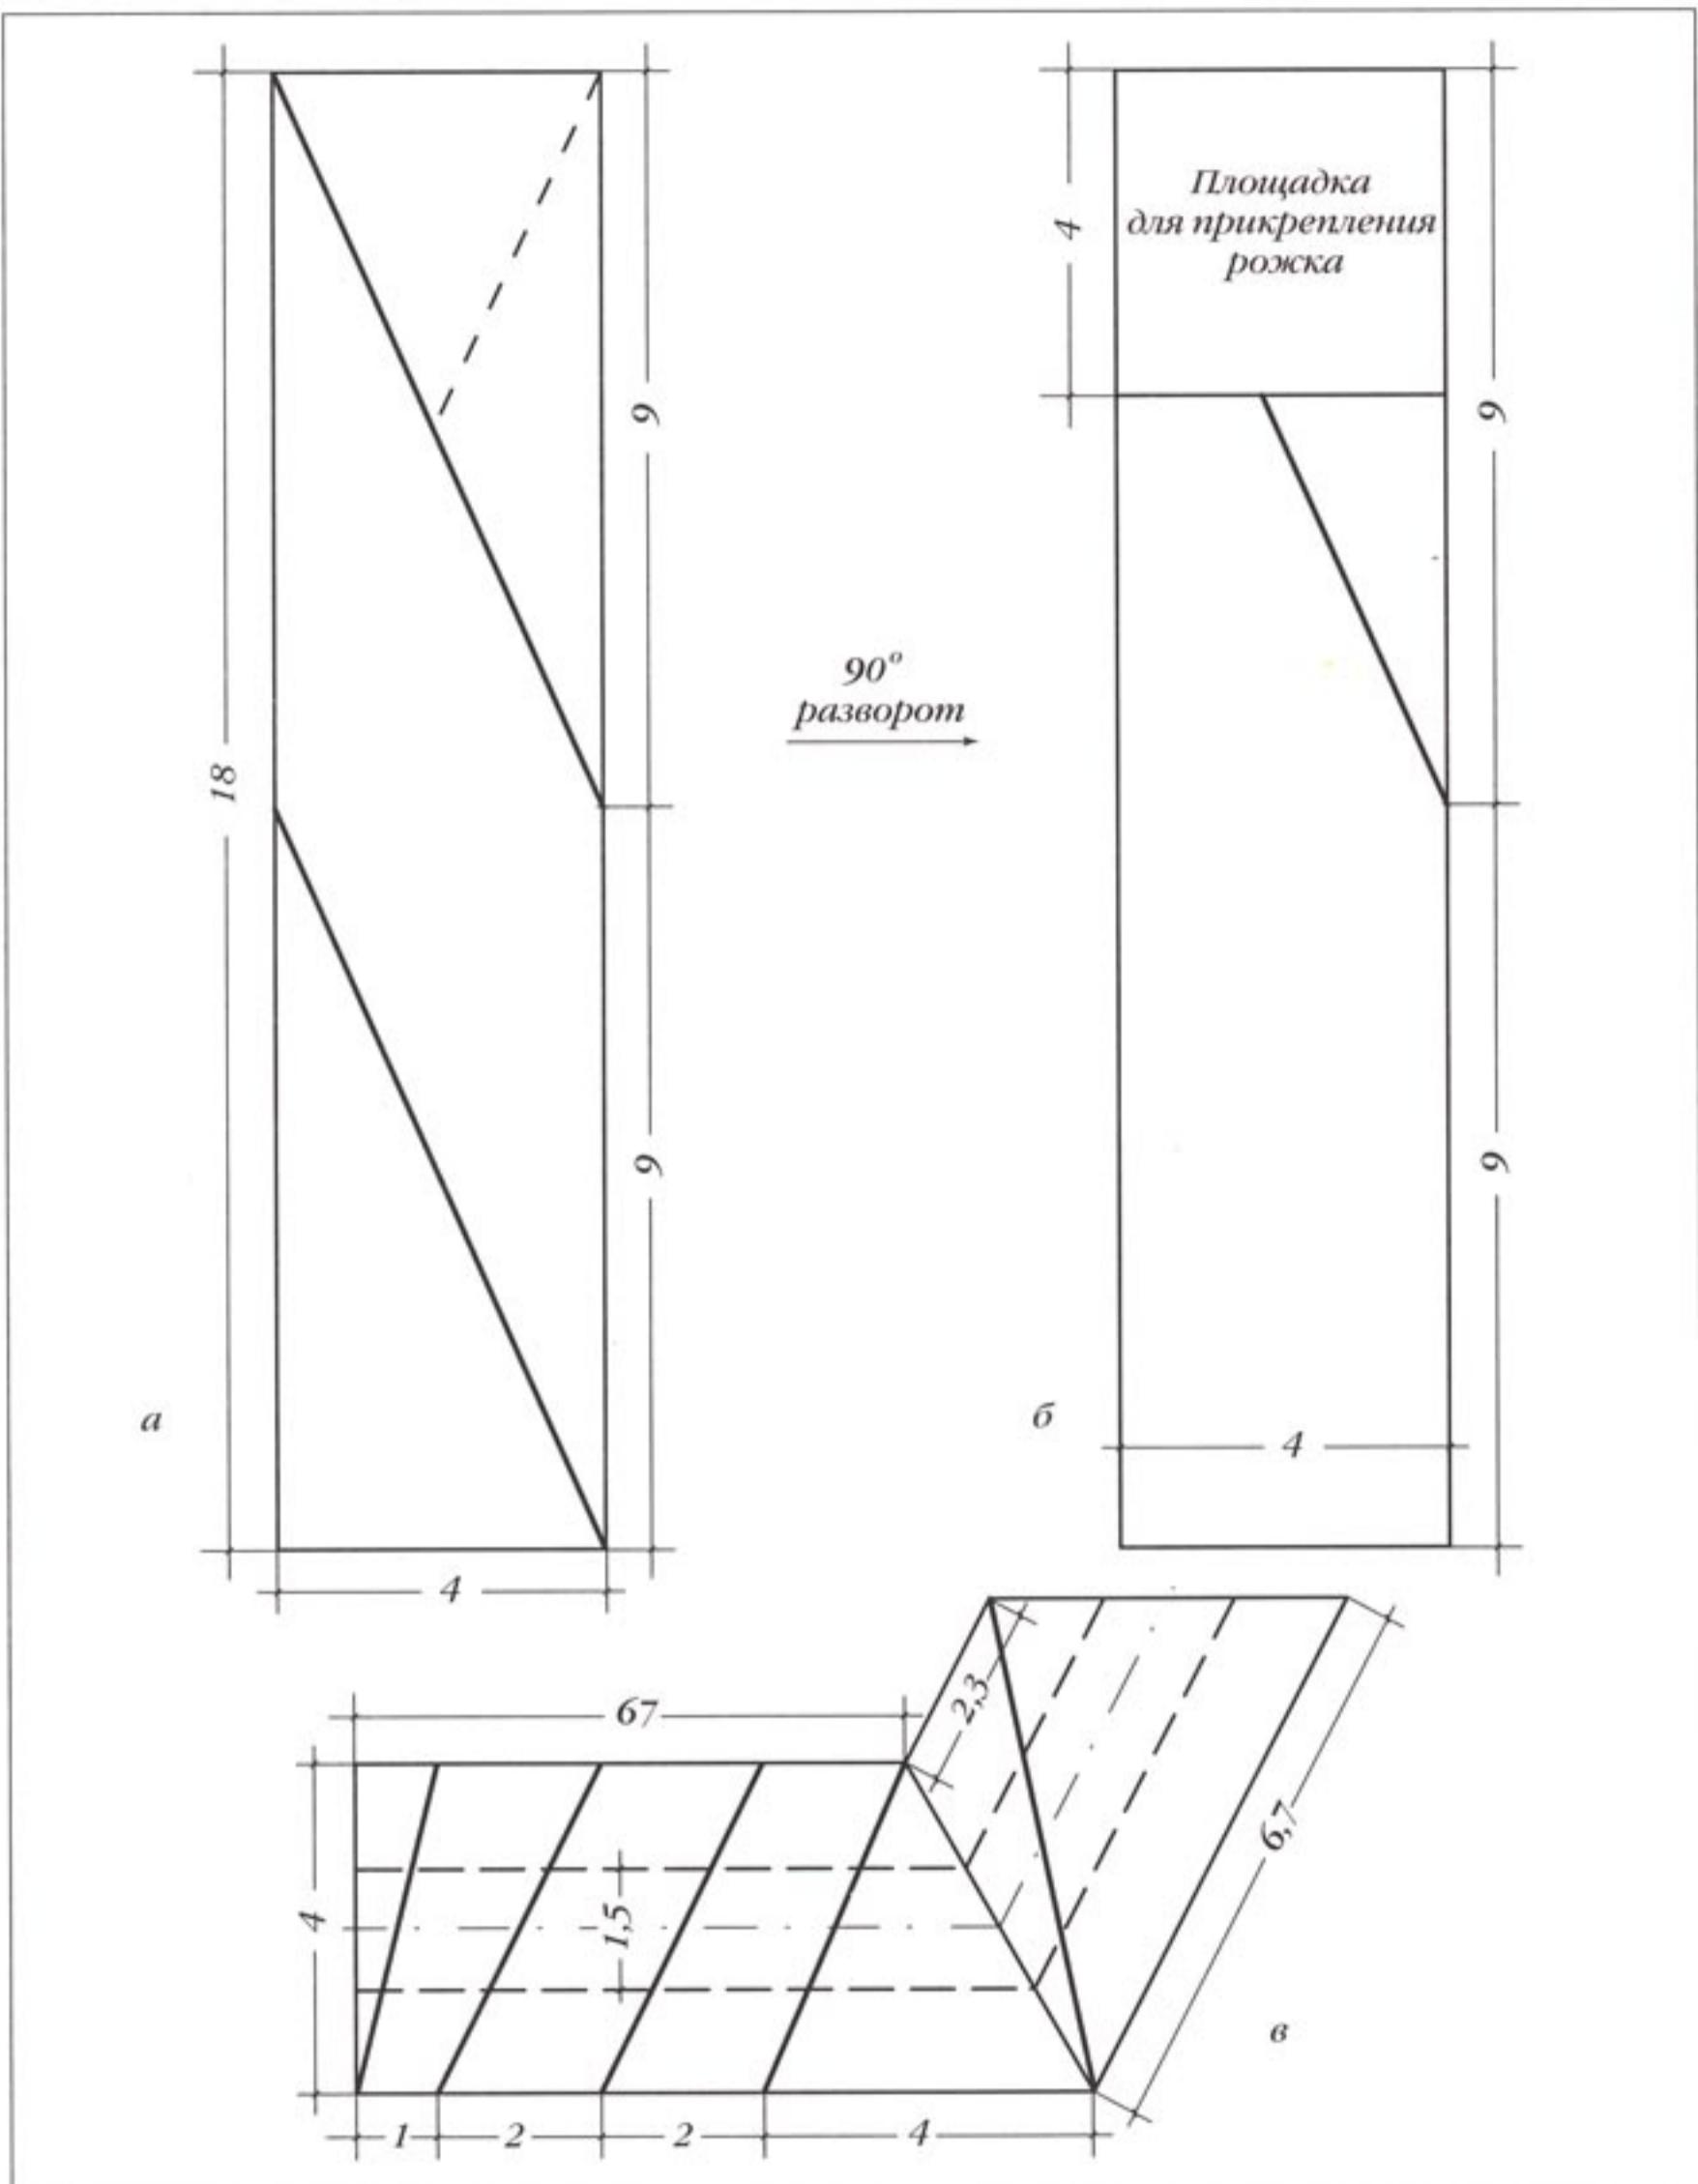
Схема разметки стойки (*a*, *b*; двухзаходный винт; шаг 9) и рожка (*c*; четырехзаходный винт) двухсвечника к рис. 175
